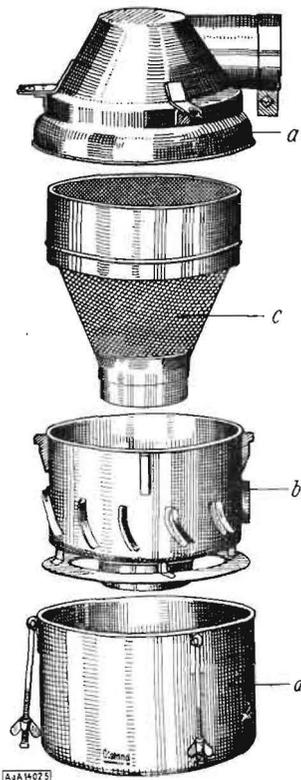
Die vier Teile des Knecht-Tornado-Wirbelöl-Luftfilters: a Deckelteil, b Einsatz, c Metallfilter, d Ölbehälter
